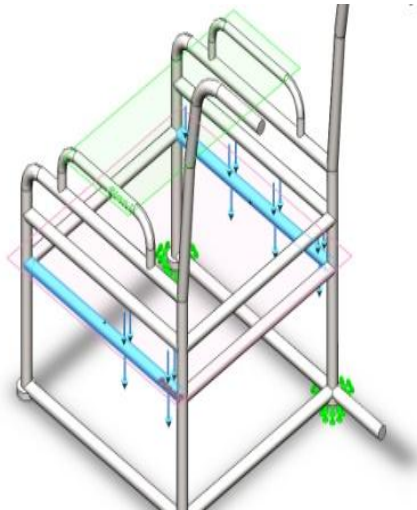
Chaise roulante simple sollicitée suivant une face par rapport au plan
